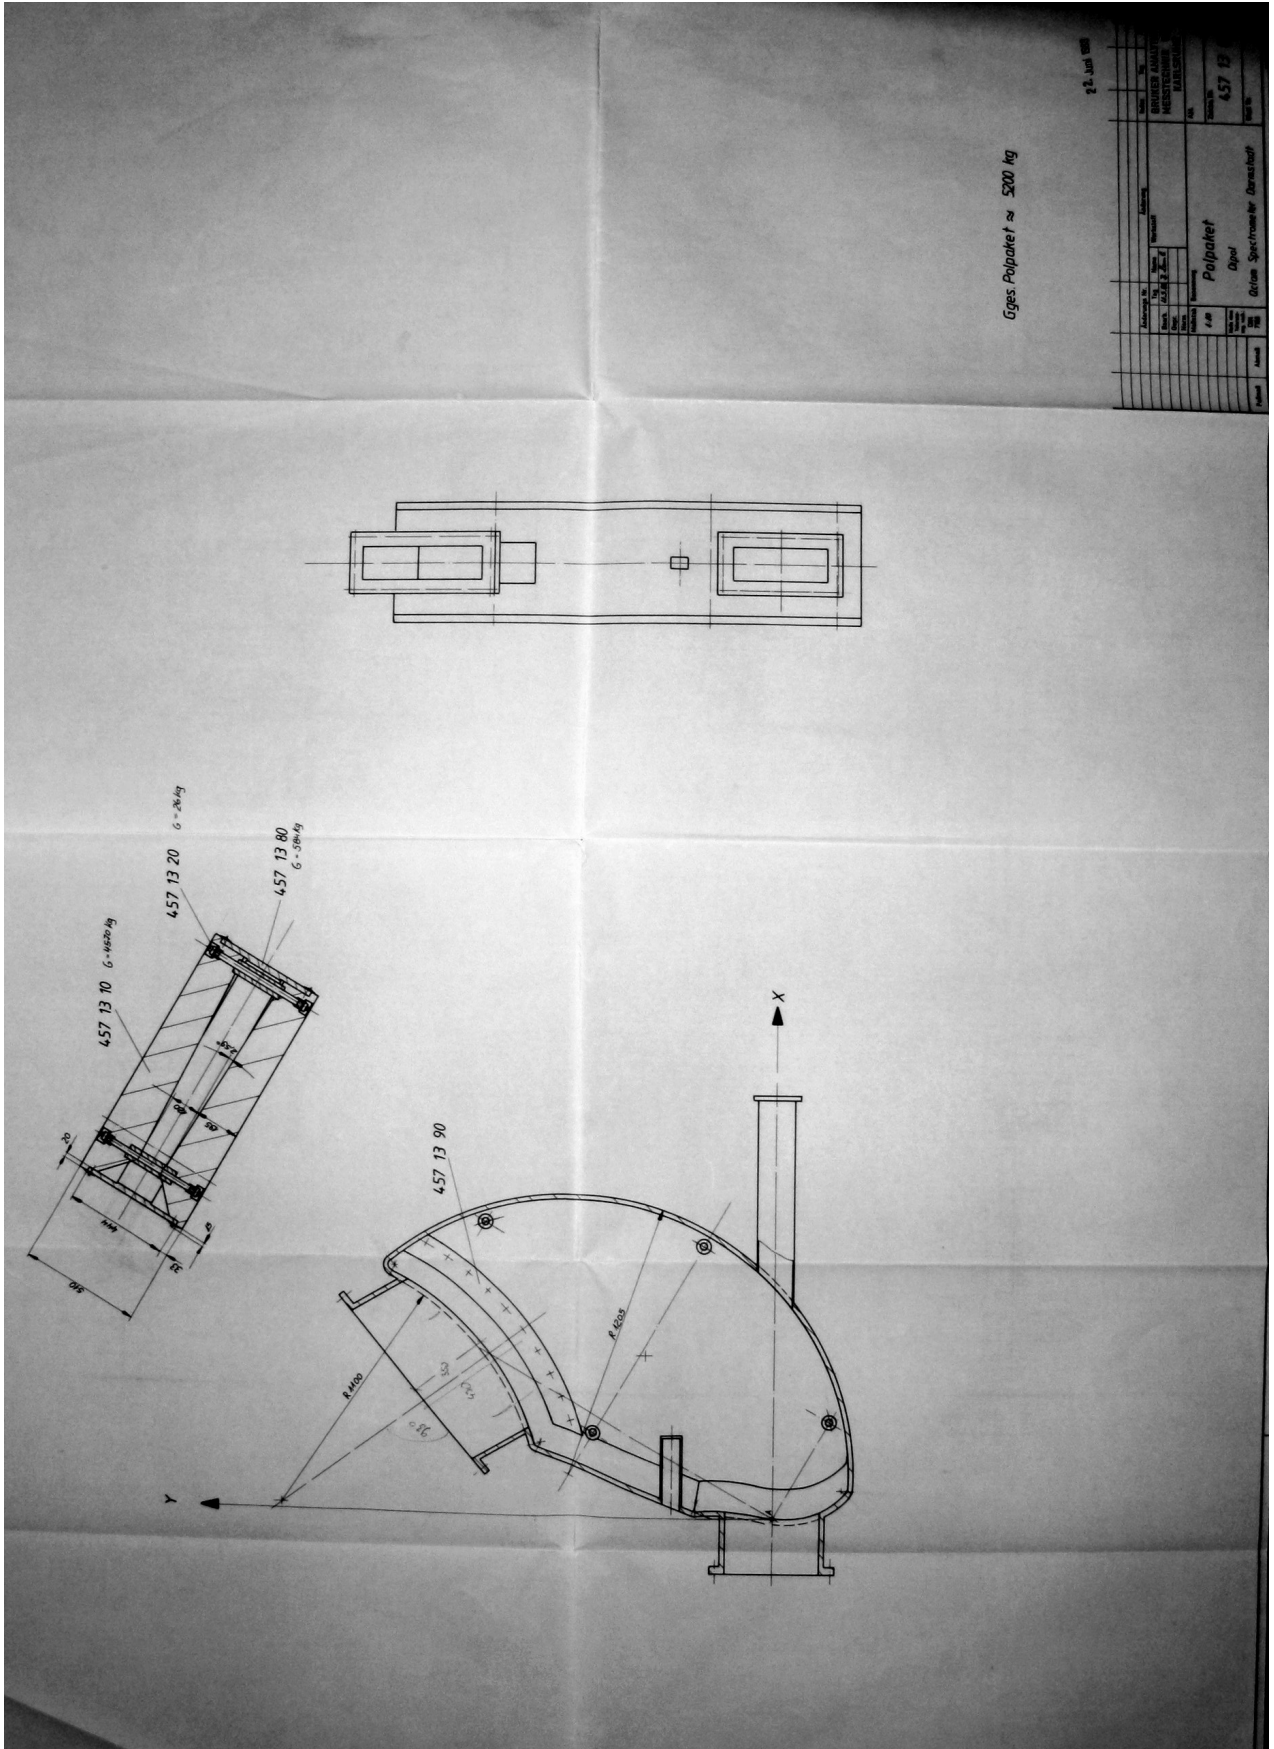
Technische Zeichnung des Polpakets des QClams.
